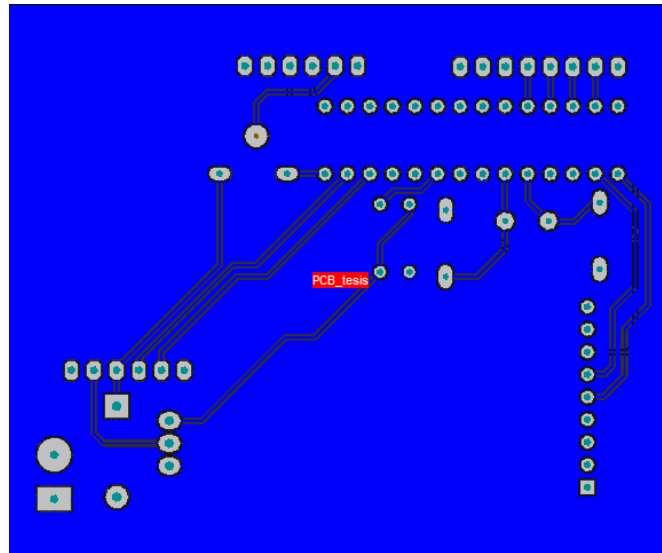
Capa Bottom Layer del layout del circuito impreso. Fuente: Elaboración propia.
